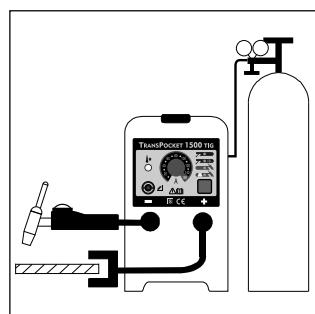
TP 1500 TIG оснащенный сварочной горелкой AL1500
